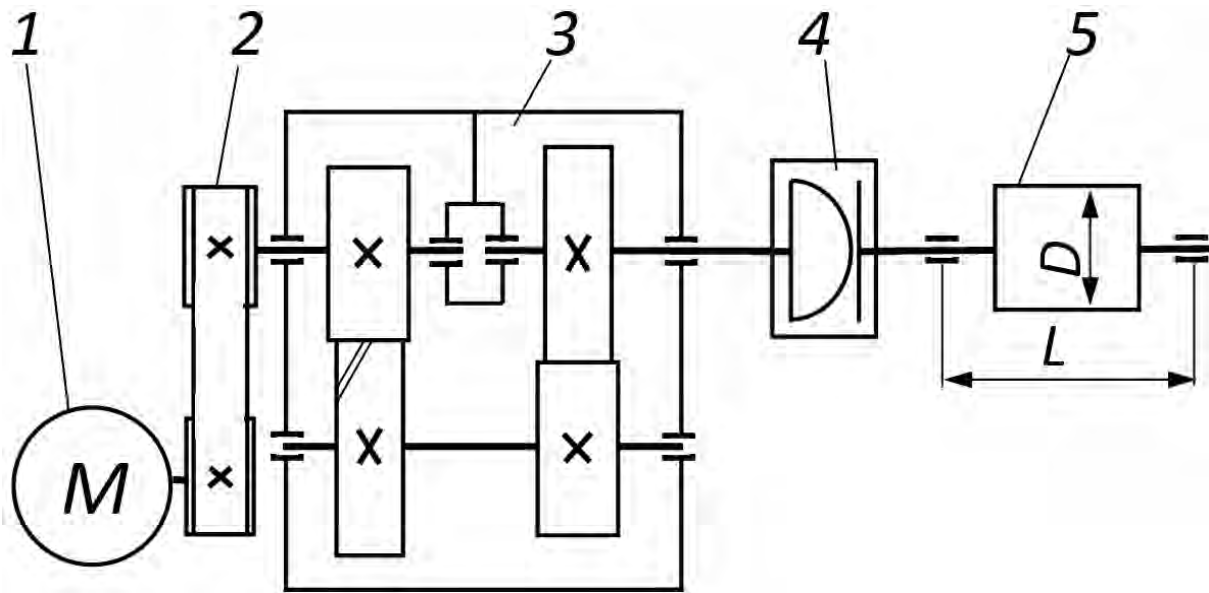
Схема привода ленточного конвейера (вид сверху): 1 – асинхронный электродвигатель; 2 – клиноременная передача; 3 – редуктор соосный двухступенчатый с цилиндрической косозубой быстроходной ступенью и цилиндрической прямозубой тихоходной ступенью; 4 – муфта компенсирующая жесткая зубчатая; 5 – приводной вал с барабаном
